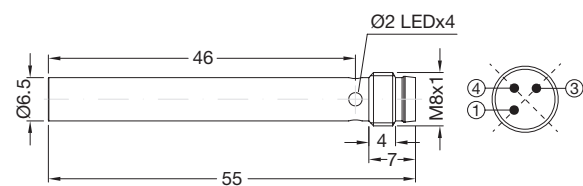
Lange Ausführung, bündiger Einbau, Steckversion
